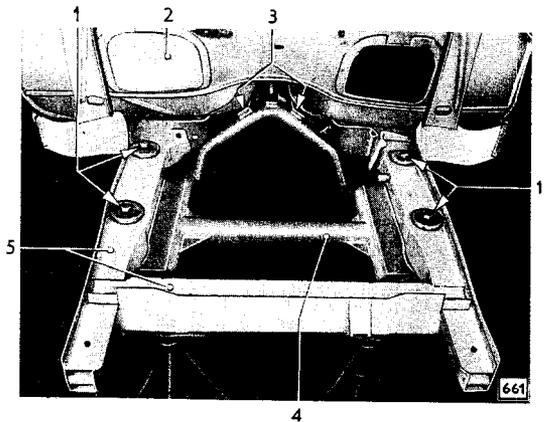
Vorderrahmen an Vorderrahmen-Schweißlehre festgeschraubt
